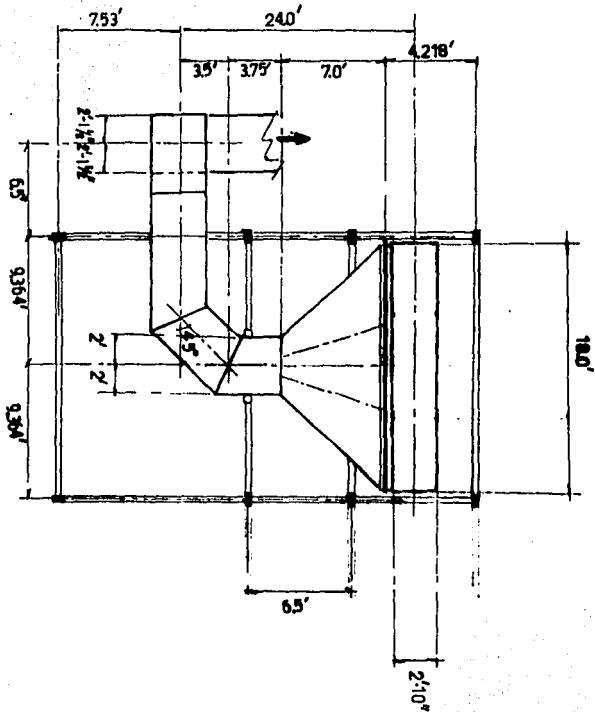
DIMENSIONES DEL CALENTADOR.
